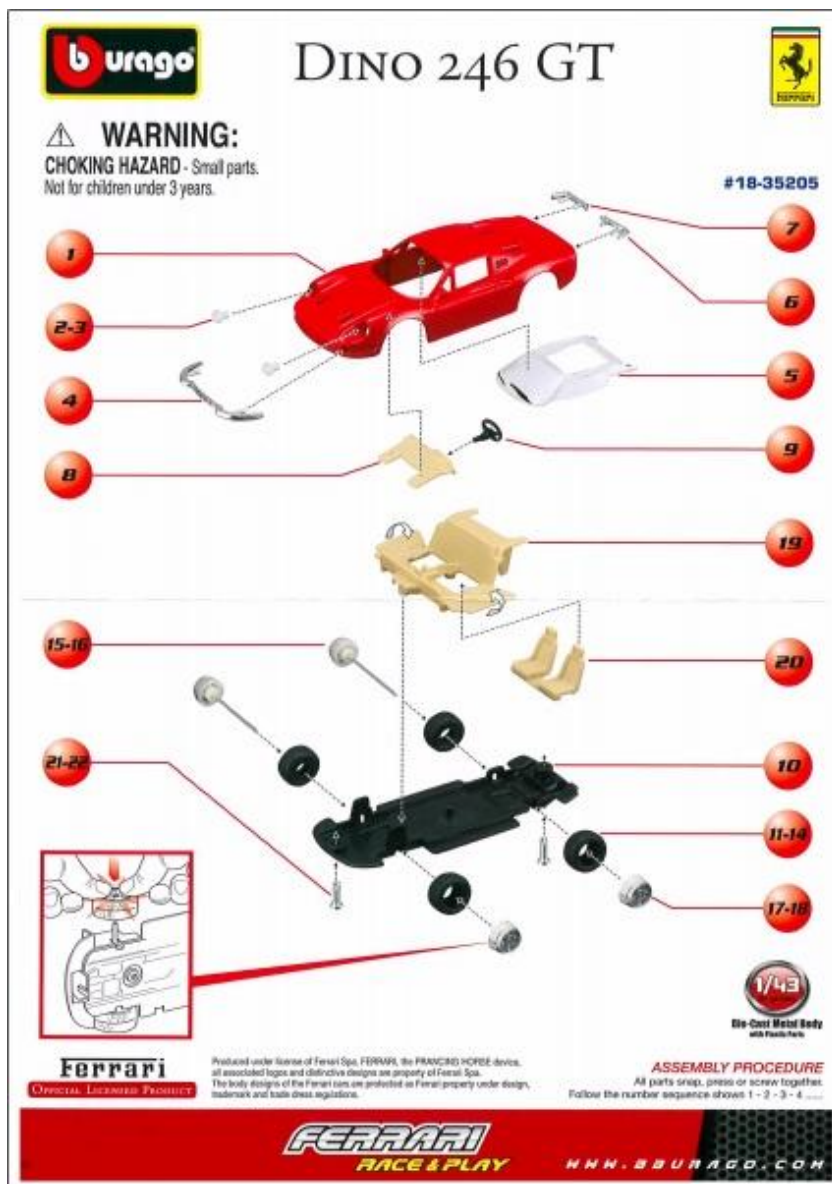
Desenho de montagem Ferrari Dino 246 GT.
